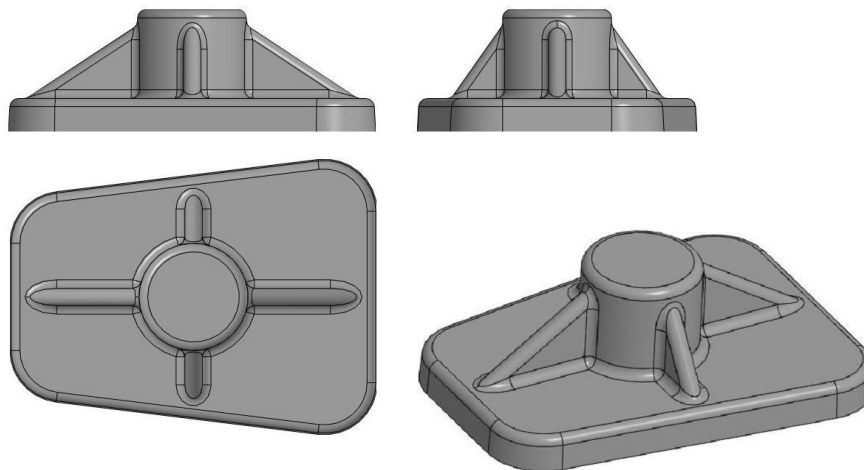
Комп'ютерна 3D-модель заготовки деталі «Кришка»
